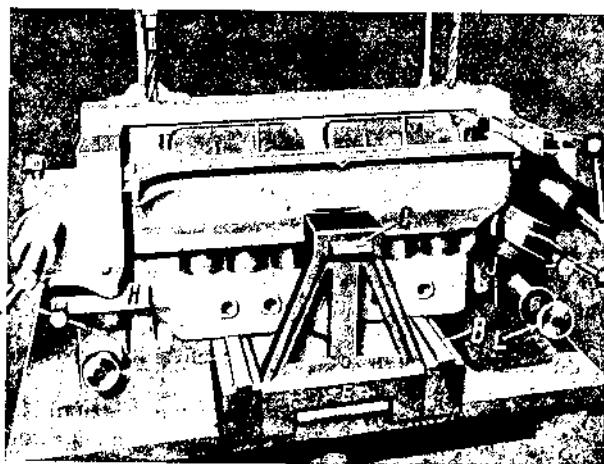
Сверление двух отверстий во фланце блока для установочных шрифтов.
